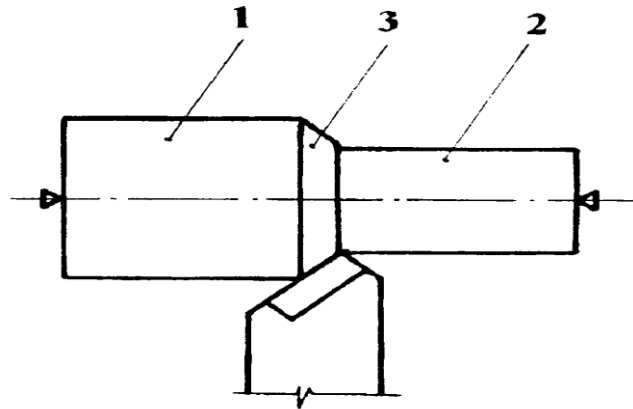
Soustava stroj – nástroj – obrobek [2]
